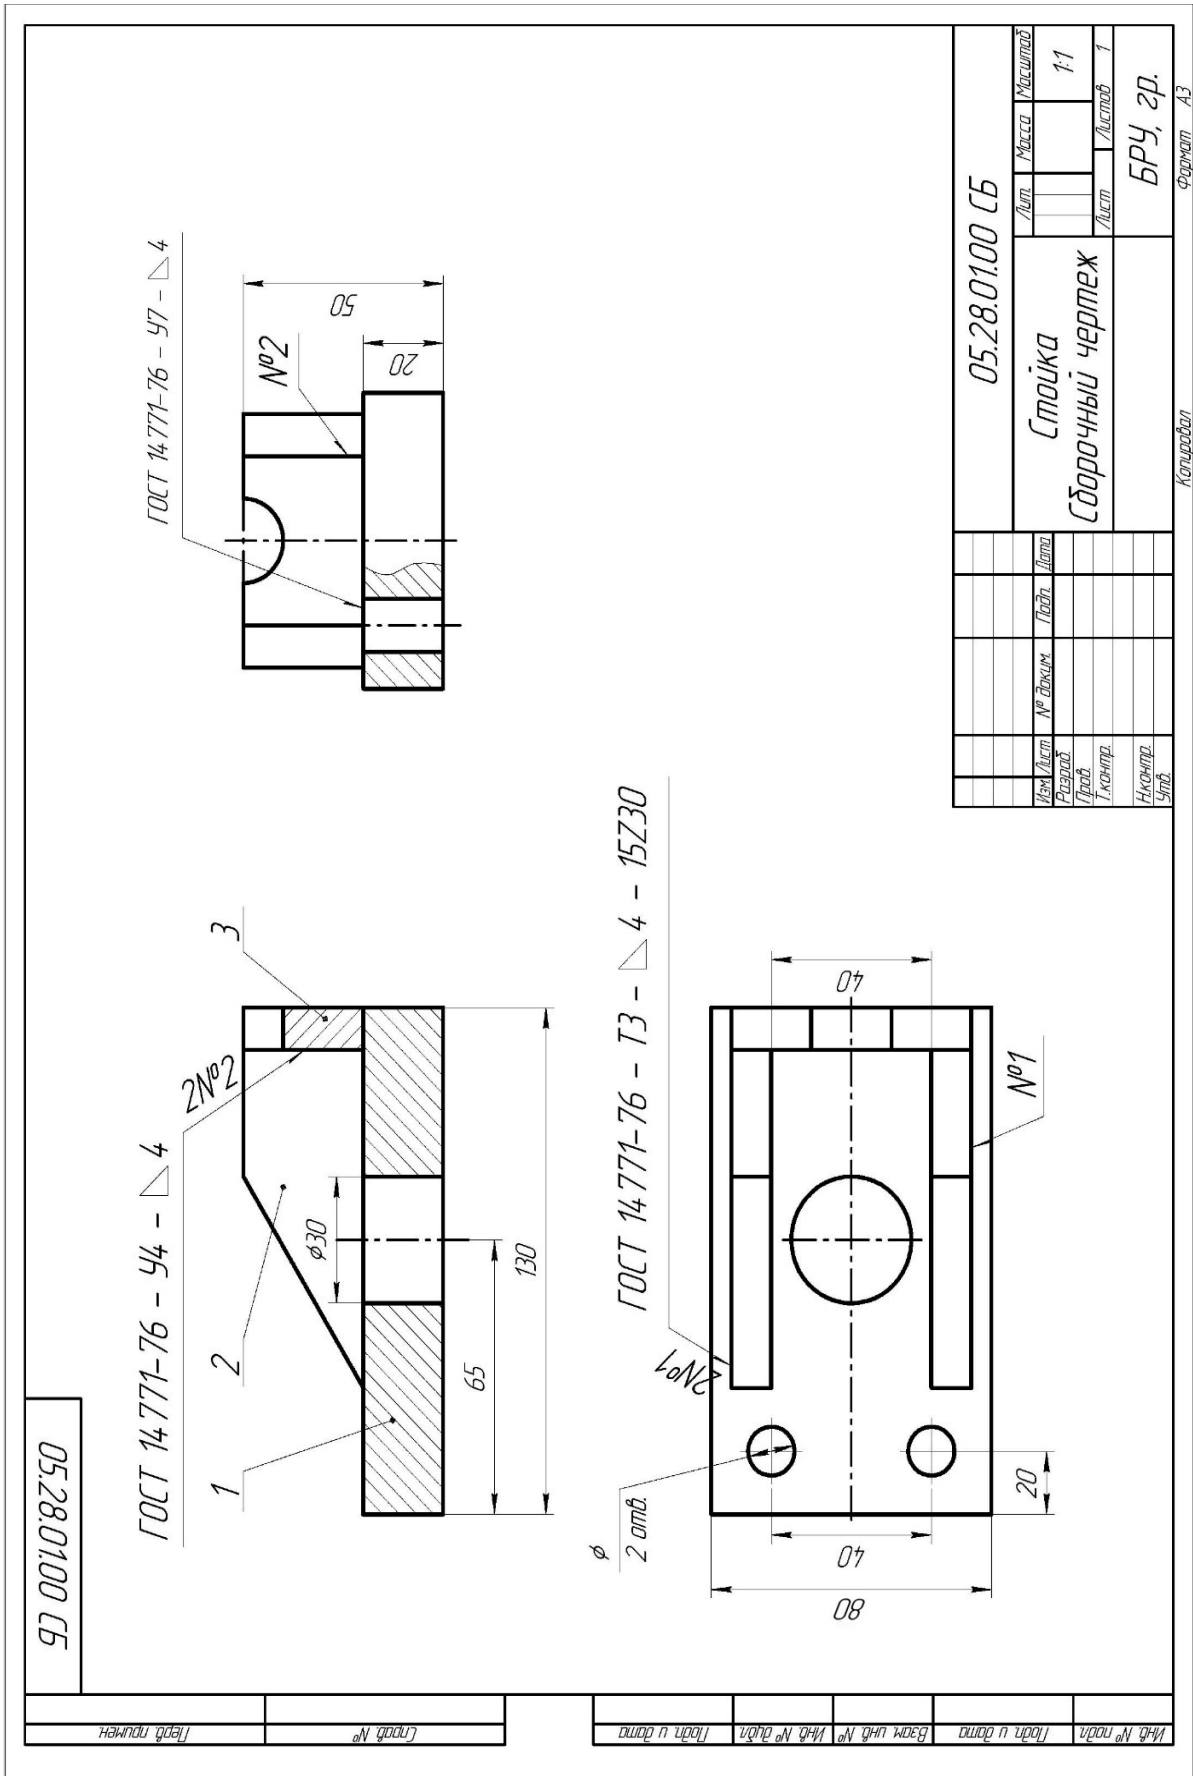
Выполненный сборочный чертеж сварного изделия «Стойка»
